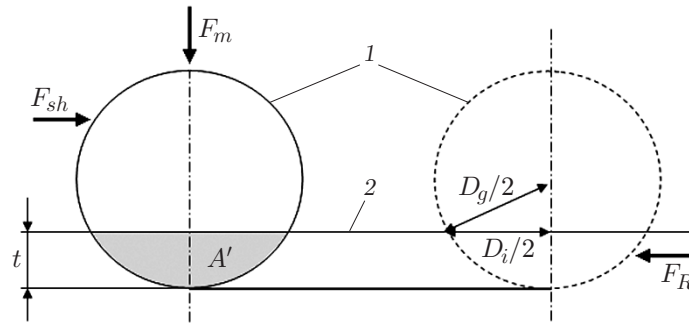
Схема резки абразивной частицей поверхности образца [8]:
